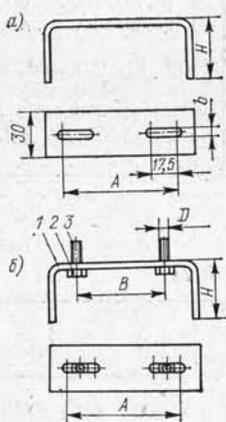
Приварные мосты для установки светильников: а — на конструкциях без зашивки изоляции; б — на конструкциях под зашивку изоляции.
